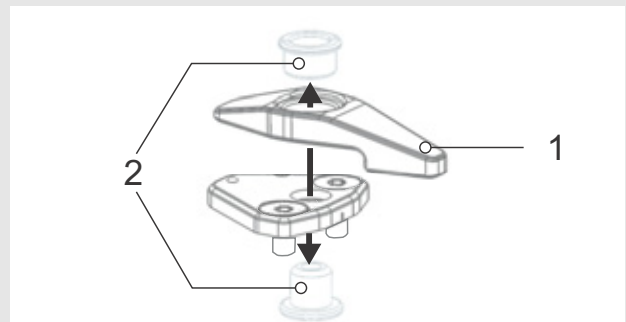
Collegamento della leva di sicurezza alla piastra di base
